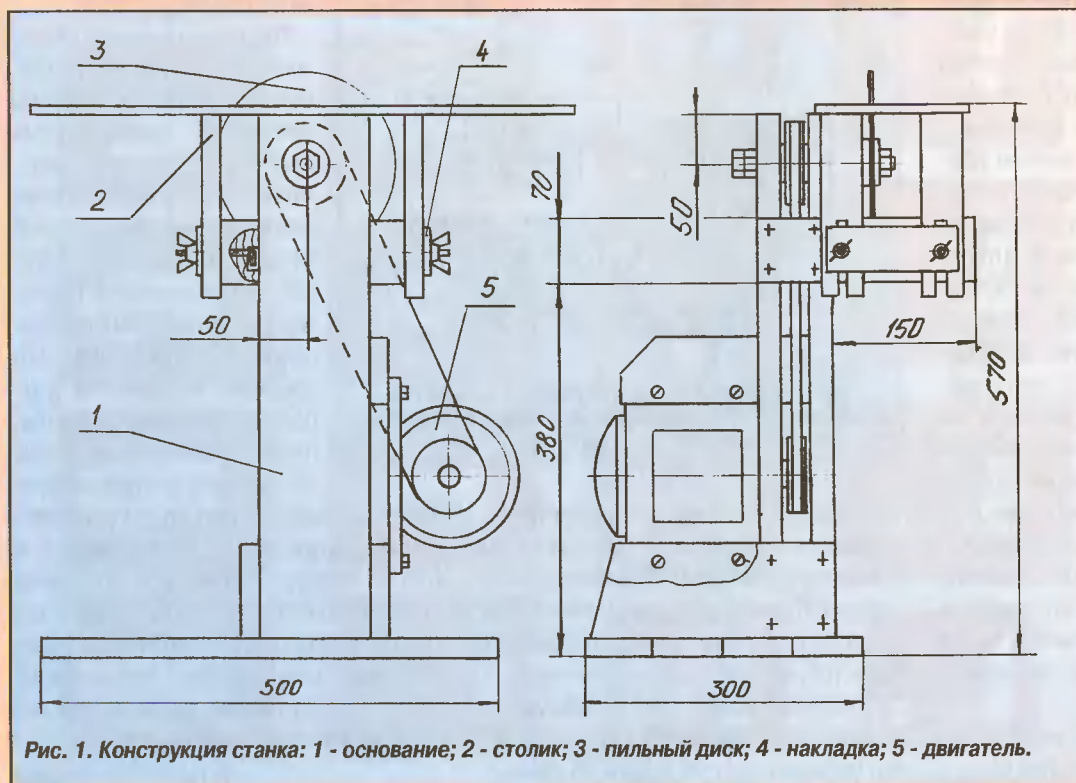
Конструкция станка: 1 - основание; 2 - столик; 3 - пильный диск; 4 - накладка; 5 - двигатель.
